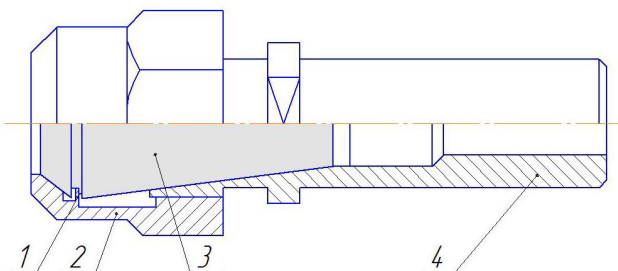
Держатель цанги ESX 16: 1 – кольцо, 2 – гайка, 3 – цанга, 4 – цанговый держатель
